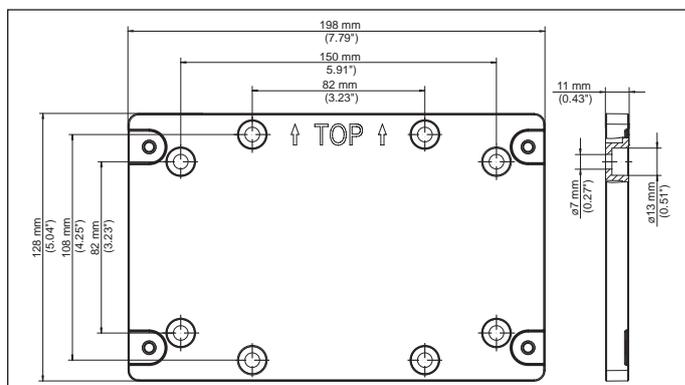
Dimensiones placa de montaje VEGAMET 861, 862
